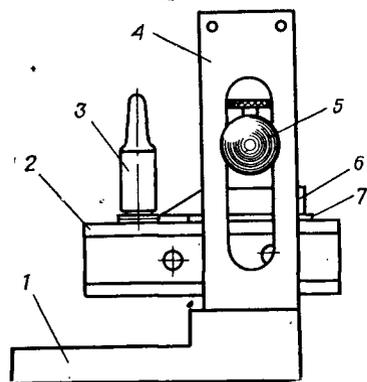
Приспособление для проверки рабочих размеров калибров: 1 — основание; 2 — линейка; 3 — калибр-шашка; 4 — струбина; 5 — прижим; 6 — боковичок; 7 — блок концевых мер (плиток)
